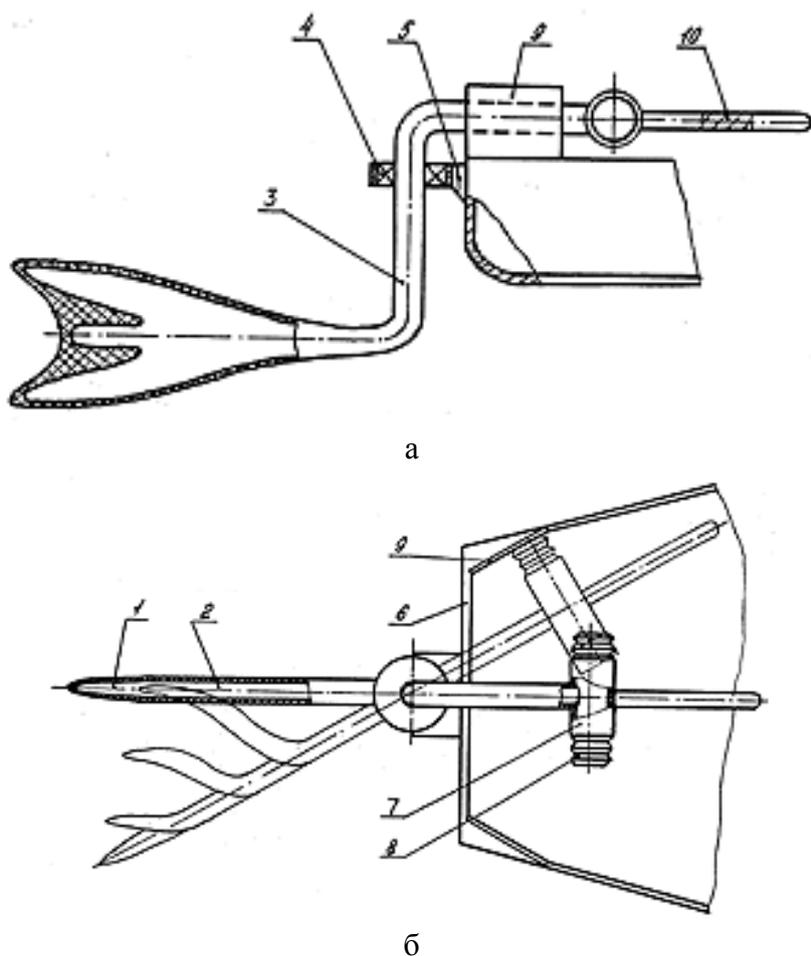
19. Лодочный машущий движитель «рыбий хвост»: а – вид сбоку, б – вид сверху
